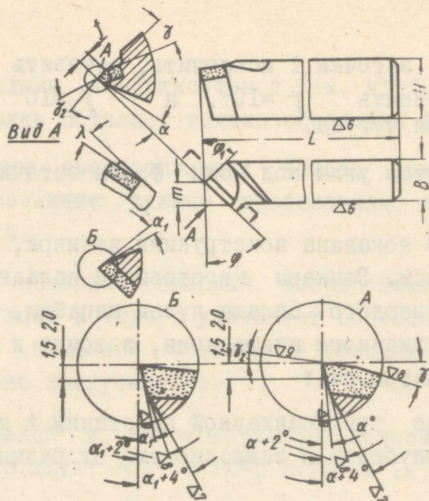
Углы заточки токарного твердосплавного резца под алмазную обработку.
